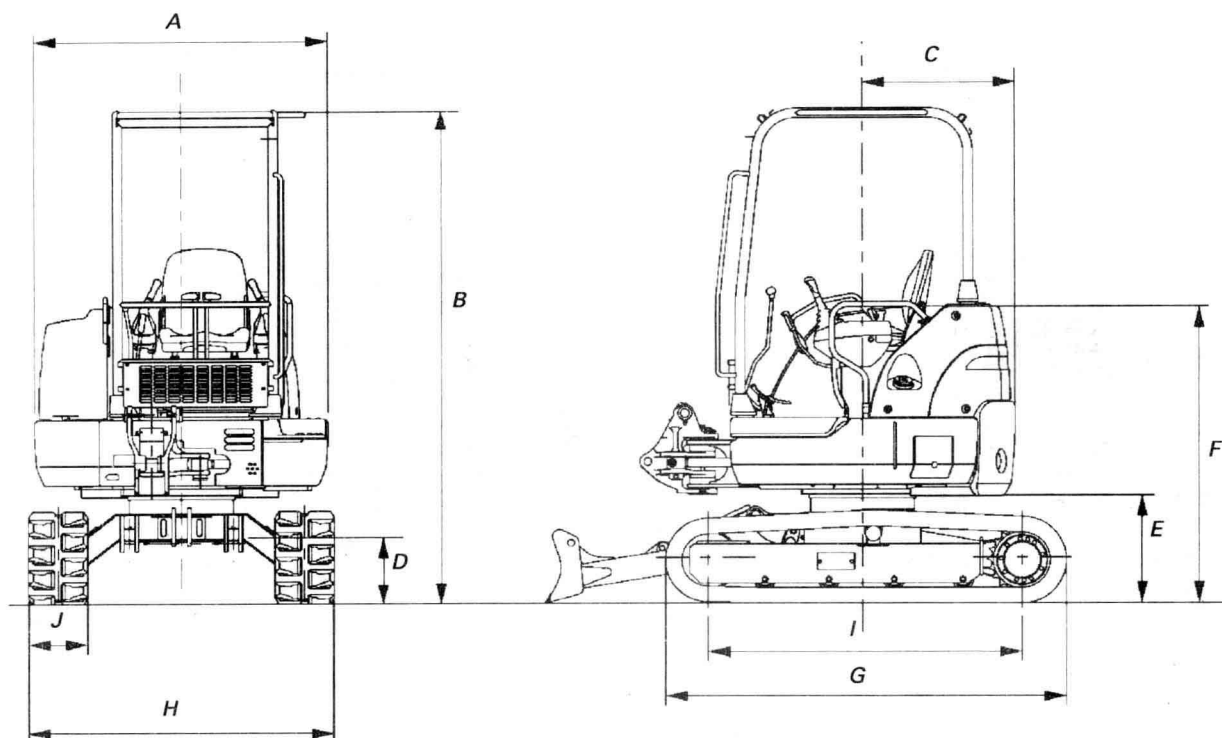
ZAXIS27U 型挖掘机外形尺寸
